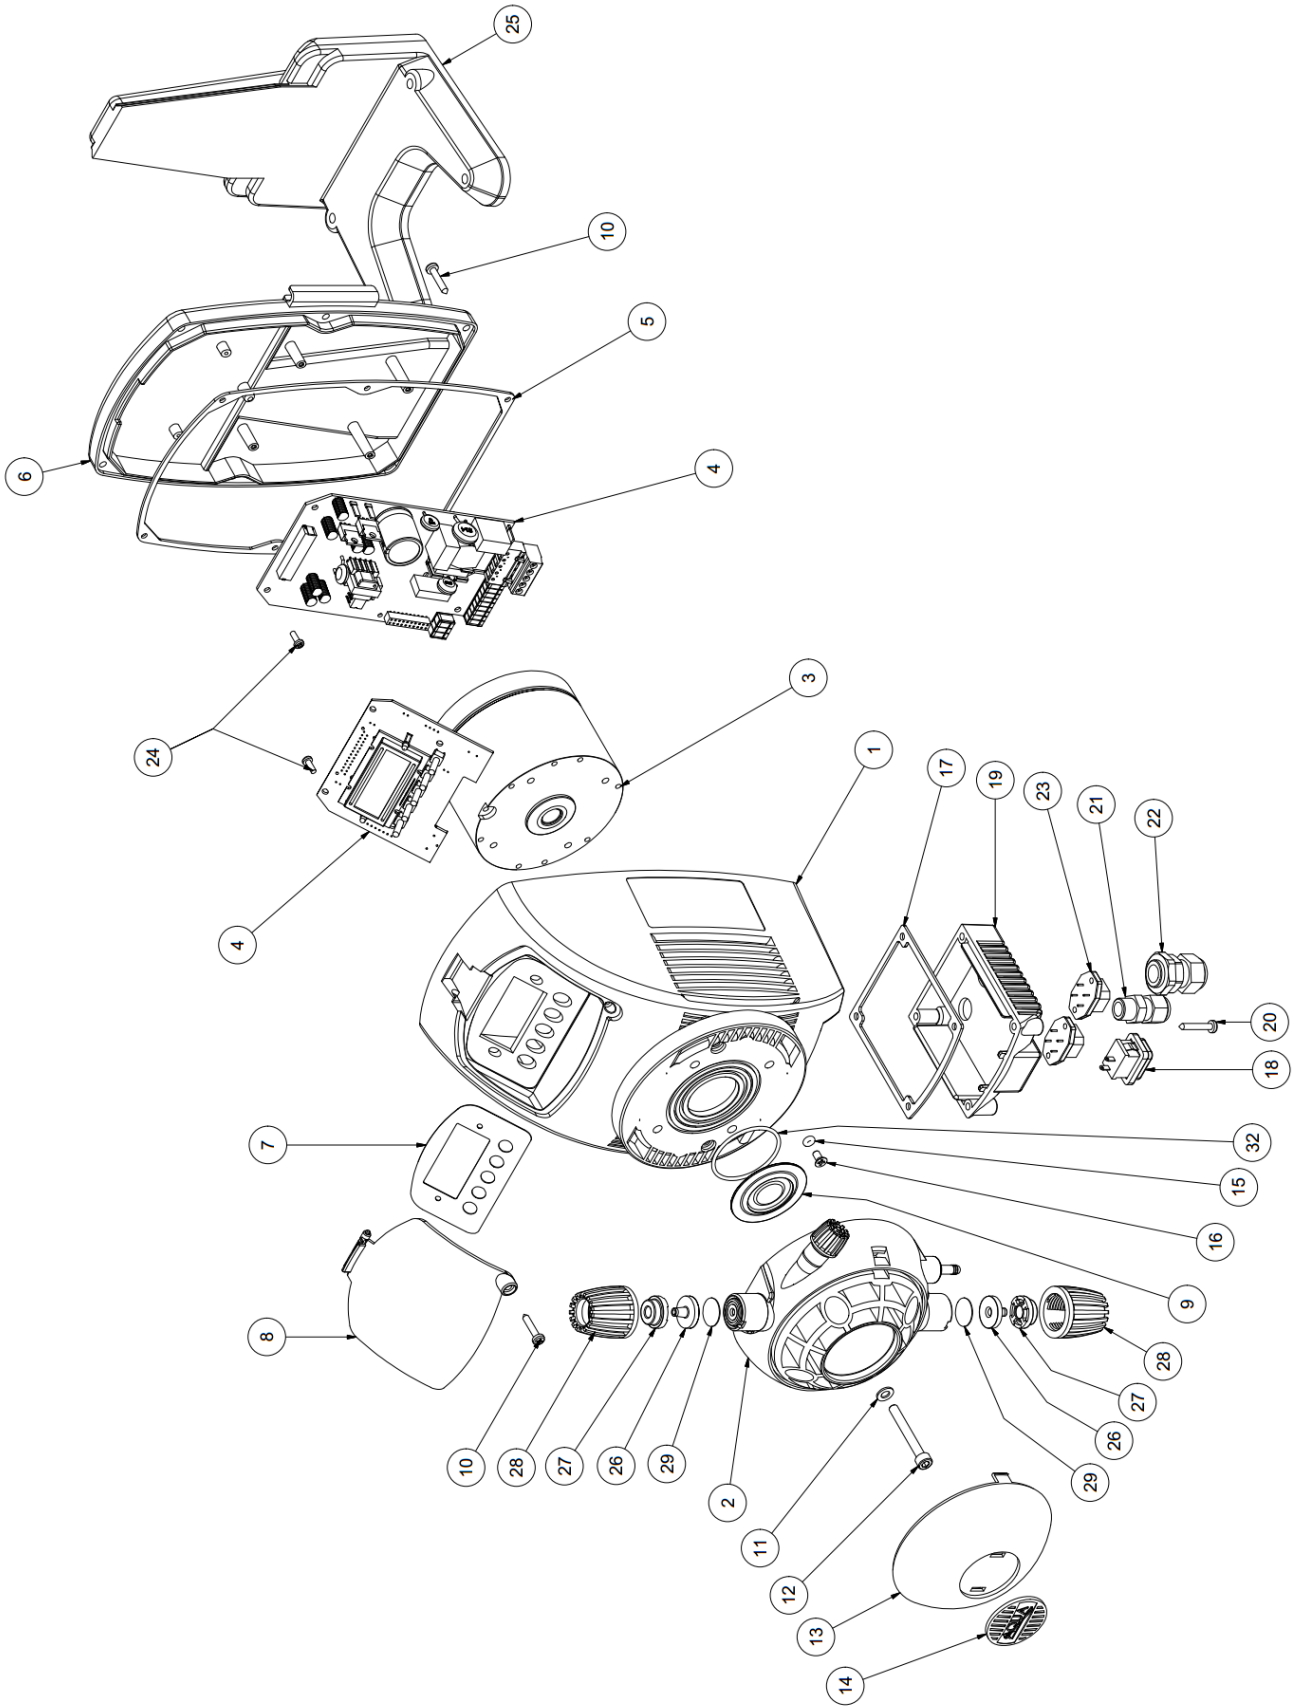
SERIE HC 899-999 - Esploso / Description / Explose / Dibujo / Explosionszeichnung /Чертеж
